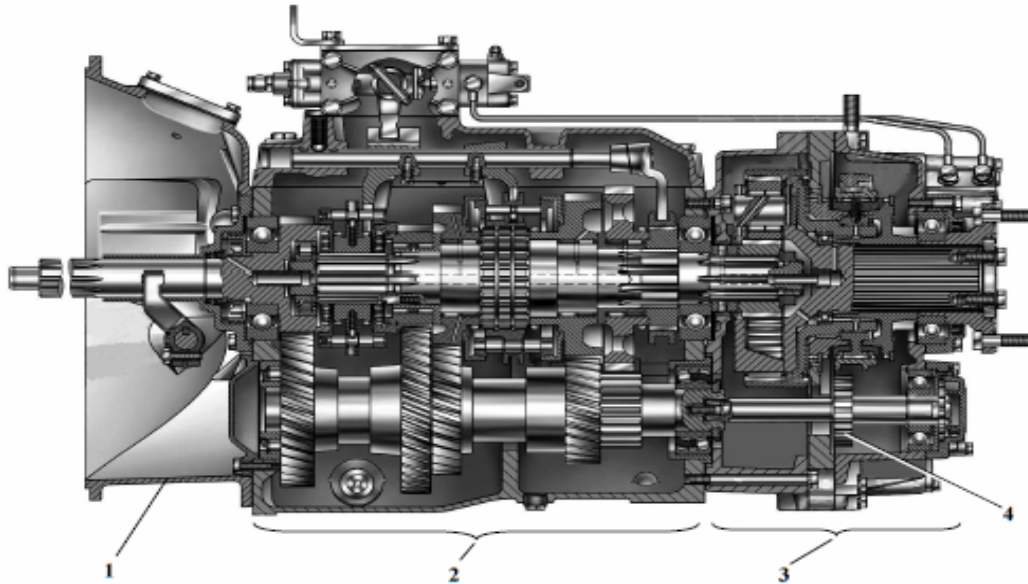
Конструкция восьмиступенчатой коробки передач КАМАЗ модели 161:
